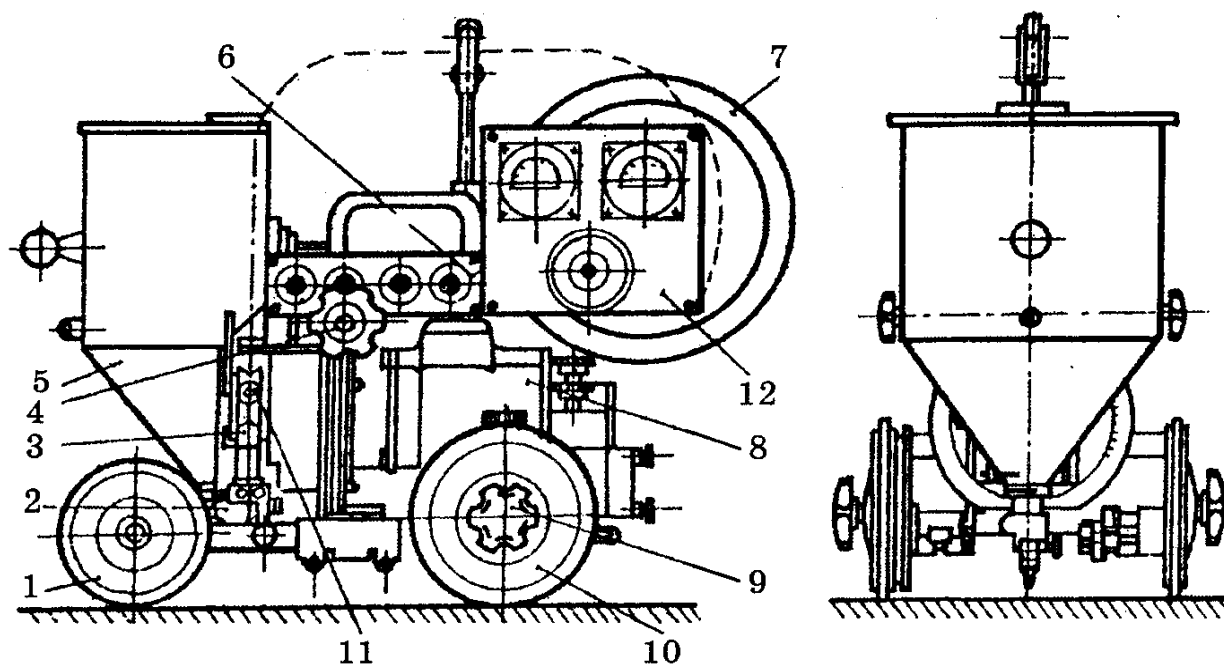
Сварочный трактор автомата АДФ-1002 УЗ
